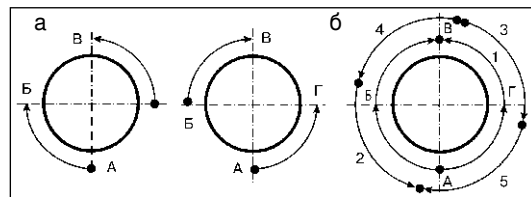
Порядок наложения первого (а) и последующих (б) слоев шва при сварке вертикального неповоротного стыка труб диаметром более 219 мм двумя сварщиками
